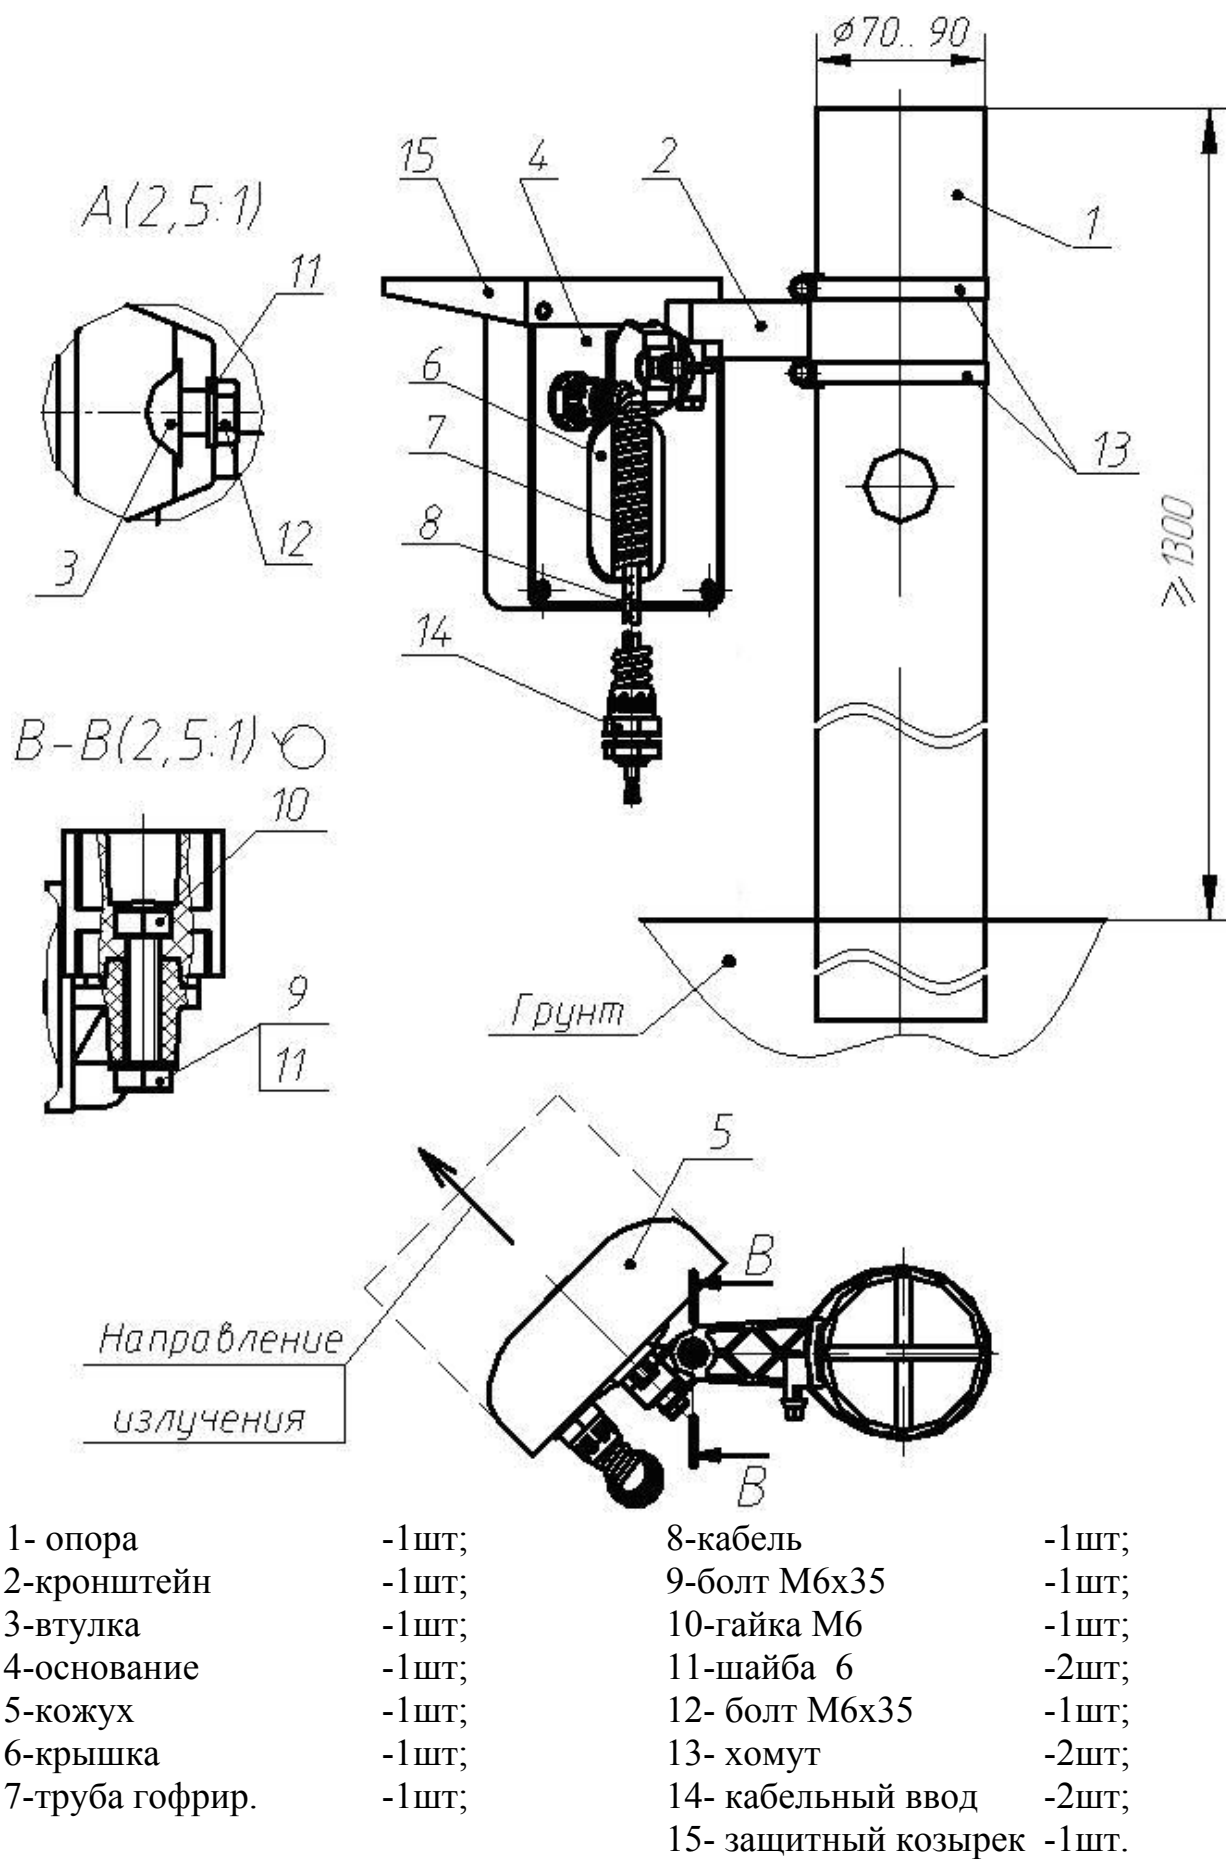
Внешний вид и установка извещателя на опоре
